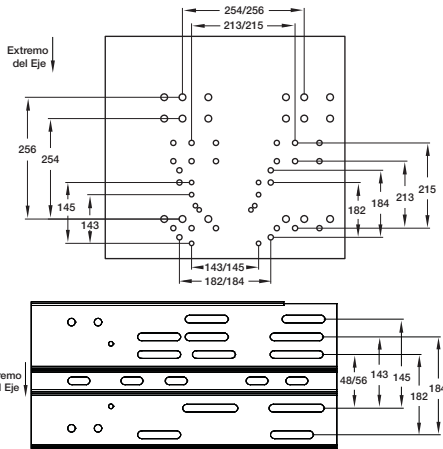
Posiciones de Montaje del Motor según el Tamaño del Bastidor del Motor
